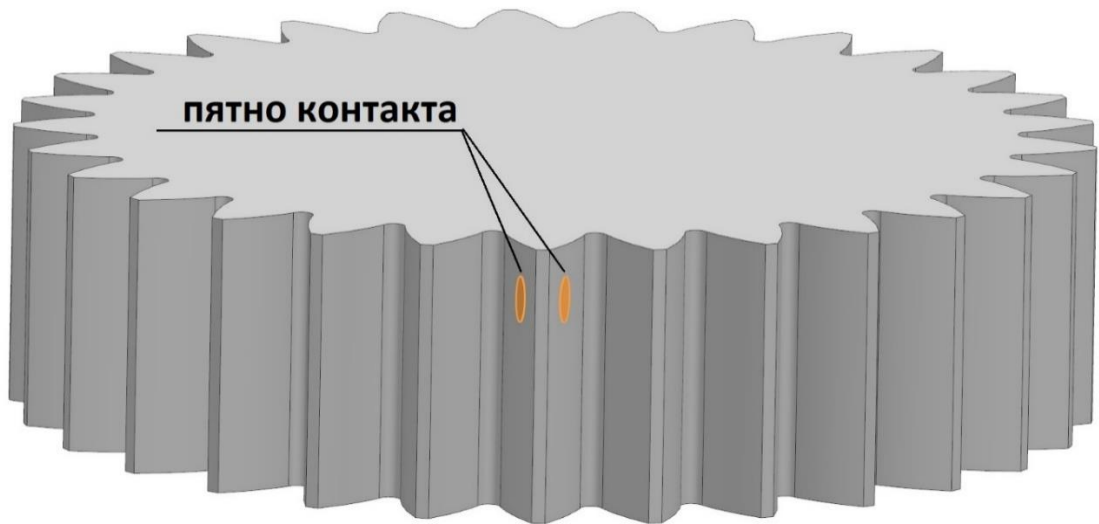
Форма пятна контакта зубчатого колеса с червячным кругом
